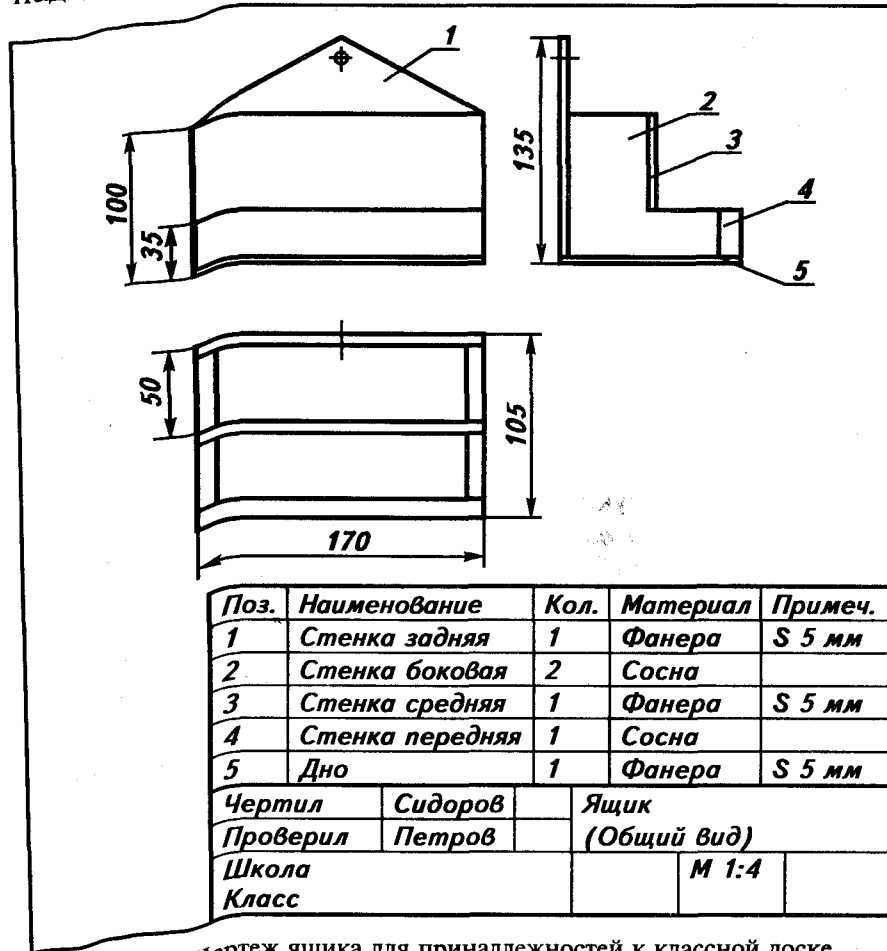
Чертеж ящика для принадлежностей к классной доске.
